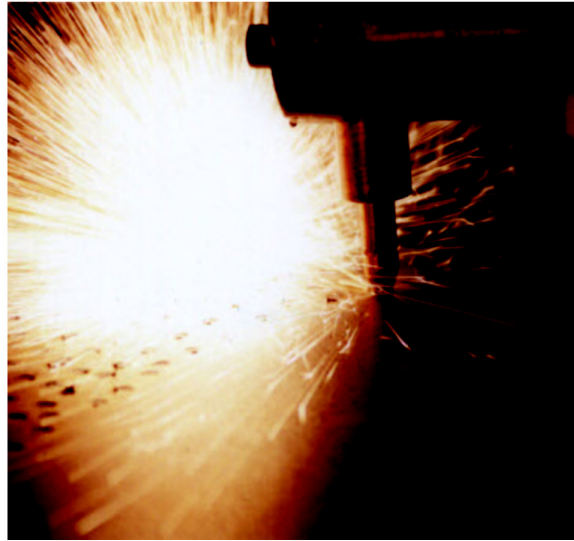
Exemplo das faíscas na hora da solda a ponto.
